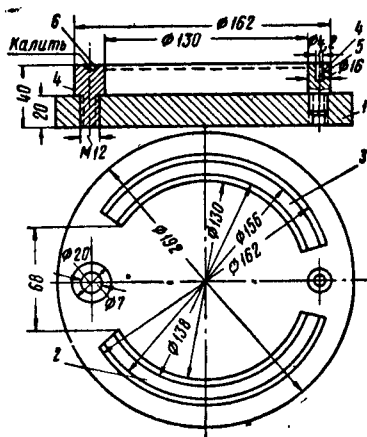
Приспособление для постановки заклепок в сепаратор подшипника 62417:
